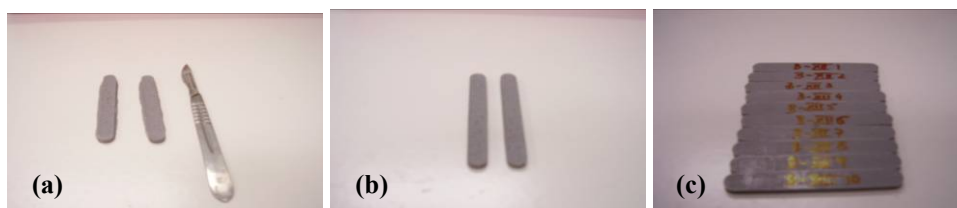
Provetes (a) após desmoldagem e bisturi; (b) aparados; (c) com numeração
